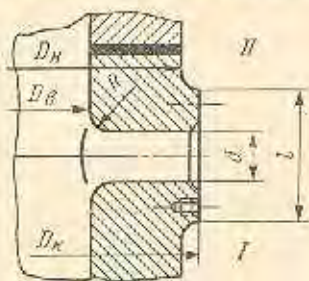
Укрепление отверстий в цилиндрической обечайке аппаратов высокого давления;
